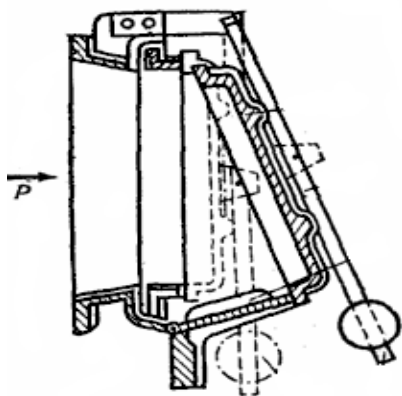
Предохранительный клапан с защитной откидной крышкой
